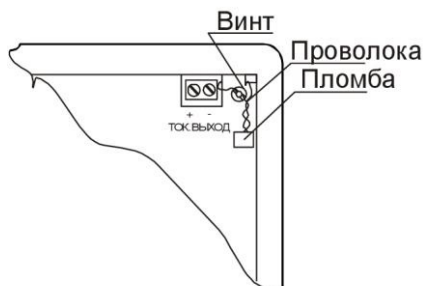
Схема пломбировки вторичного преобразователя при креплении в щит
